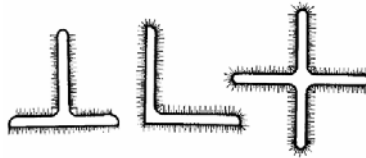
TORSIÓN Y CORTANTE COMBINADOS SOBRE PERFILES CON SOLDADURA PERIMETRAL
